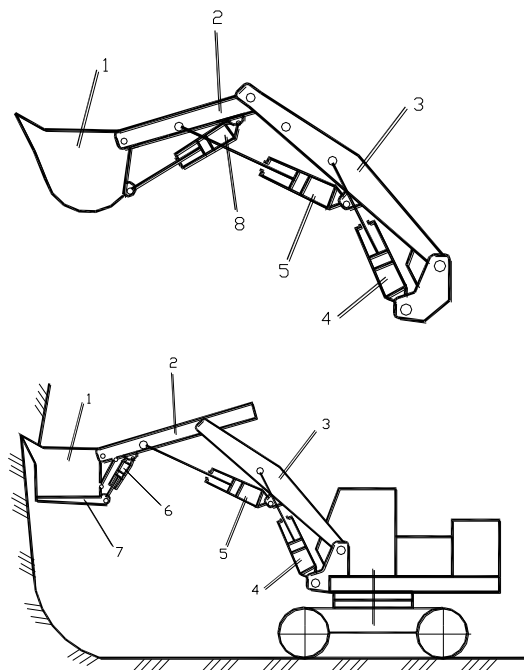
Рабочее оборудование экскаватора с прямой лопатой с жесткой подвеской
